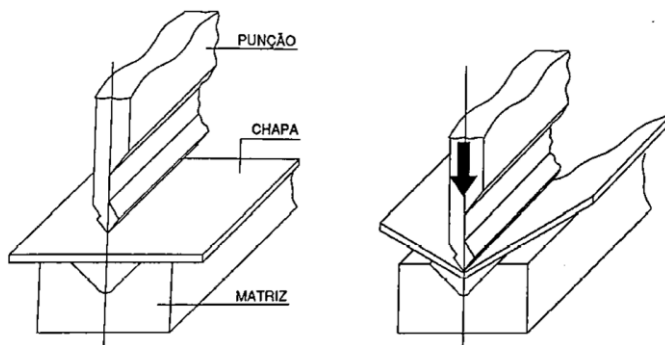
Posições relativas da chapa durante o processo de quinagem e das ferramentas utilizadas [4].
